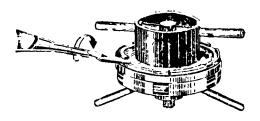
Разборка муфты сцепления при помощи приспособления.
